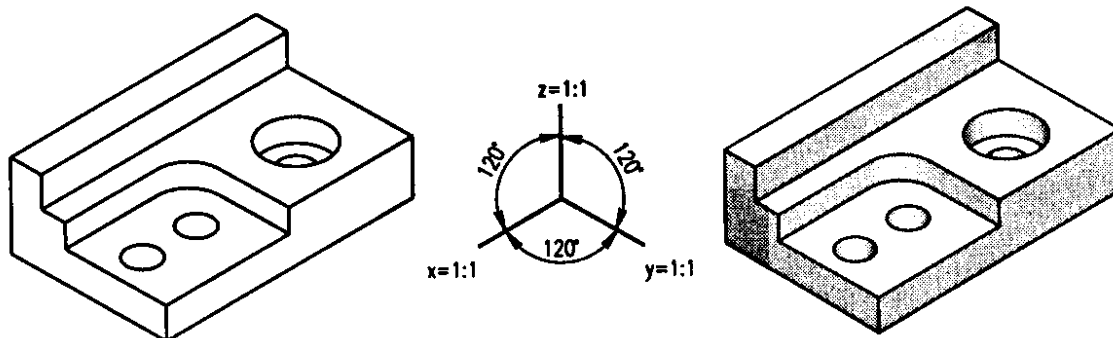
, Technická izometrie (pravoúhlá)
